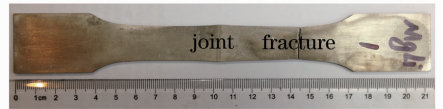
Mg-9.8Li-2.9Al-Zn 合金焊接接头纵向拉伸断裂宏观形貌
